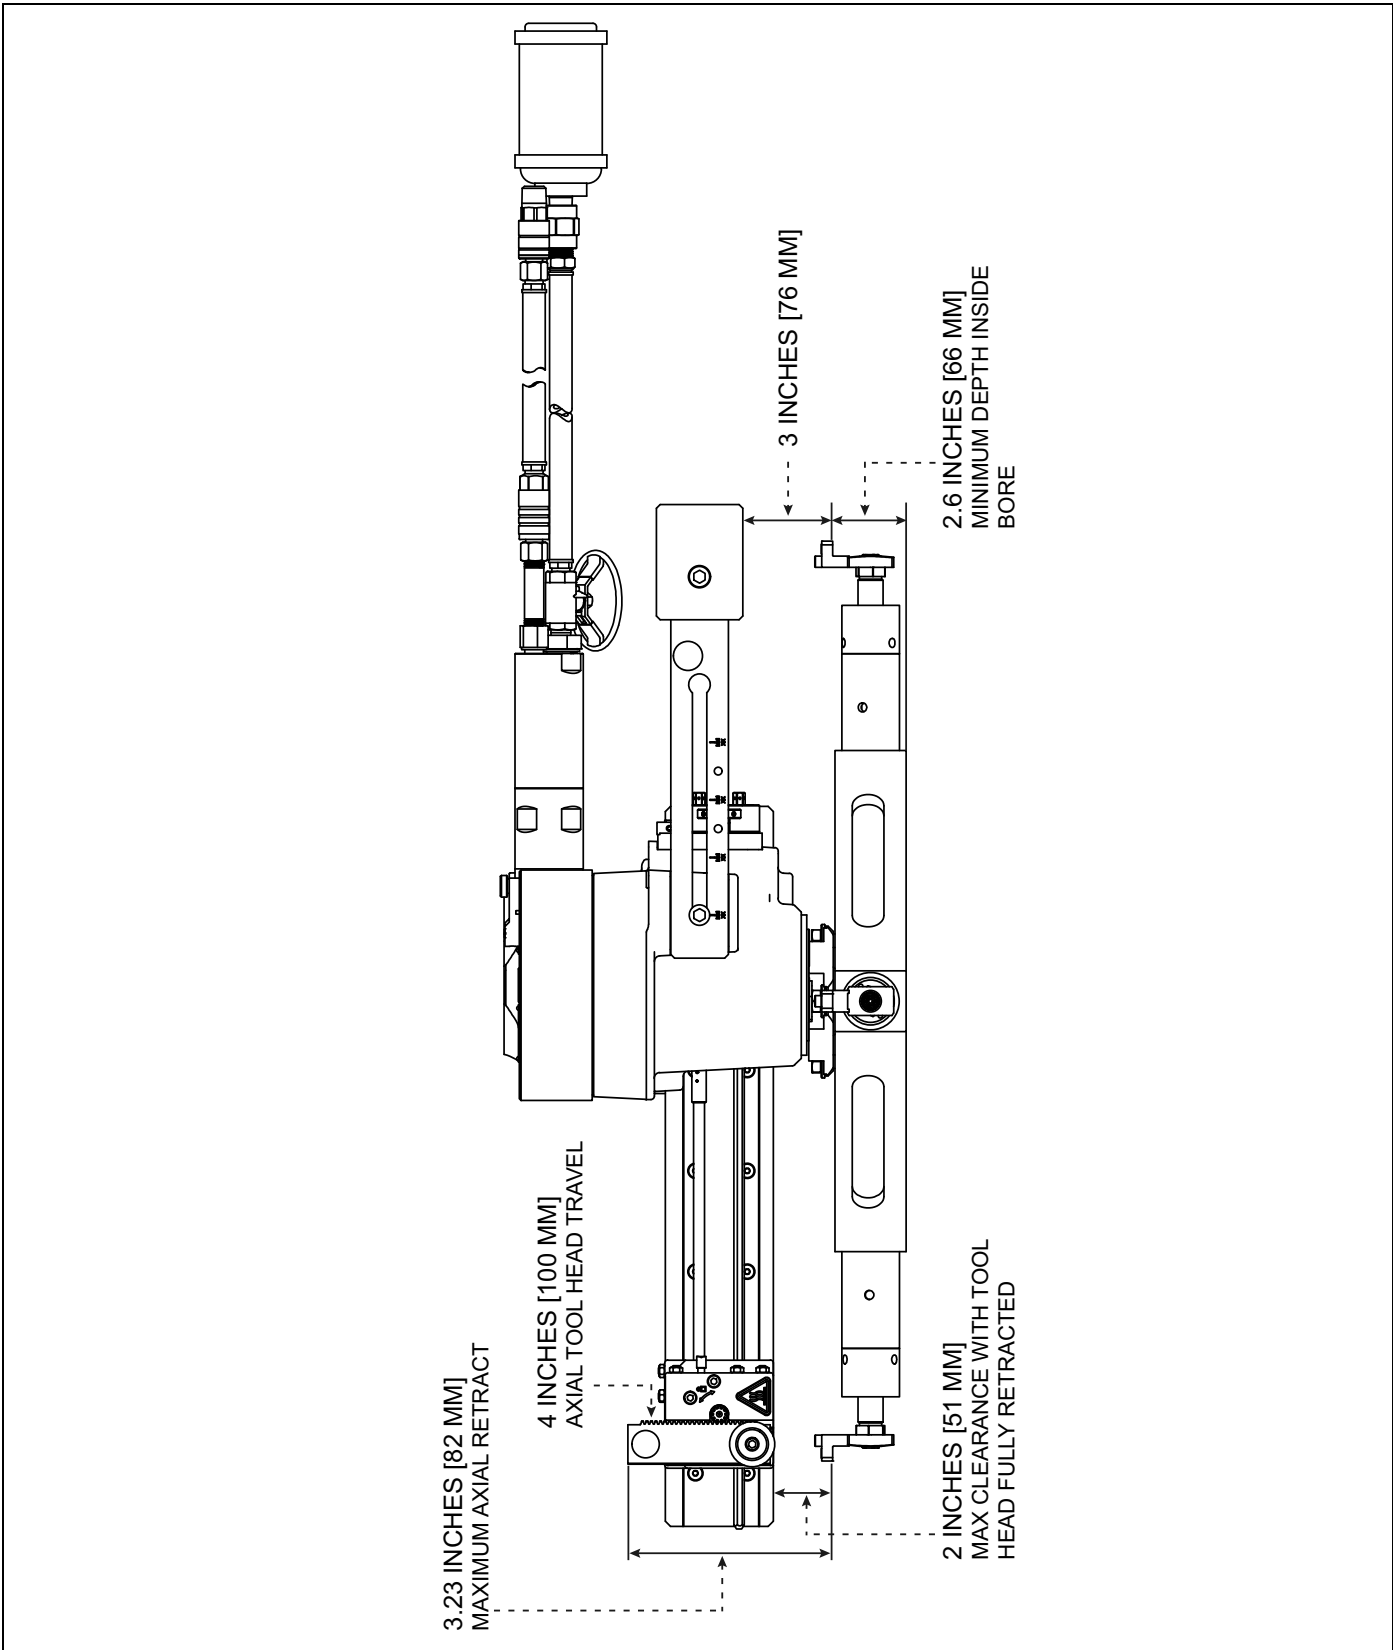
РАЗМЕРЫ, ВИД СБОКУ
